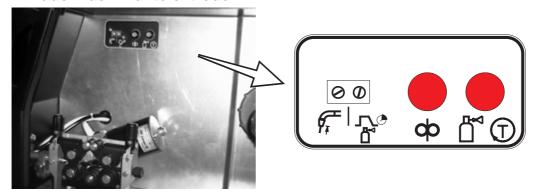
/2: Bedienelemente im Inneren des Schweißgerätes bzw. DV- Koffer
